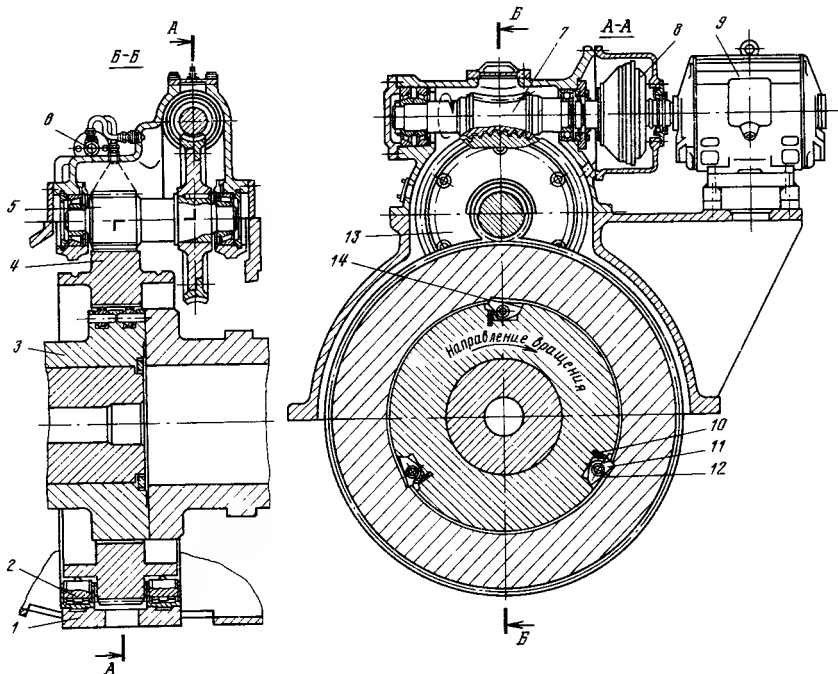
Валоповоротное устройство турбины К-500-65/3000 ХТЗ:
